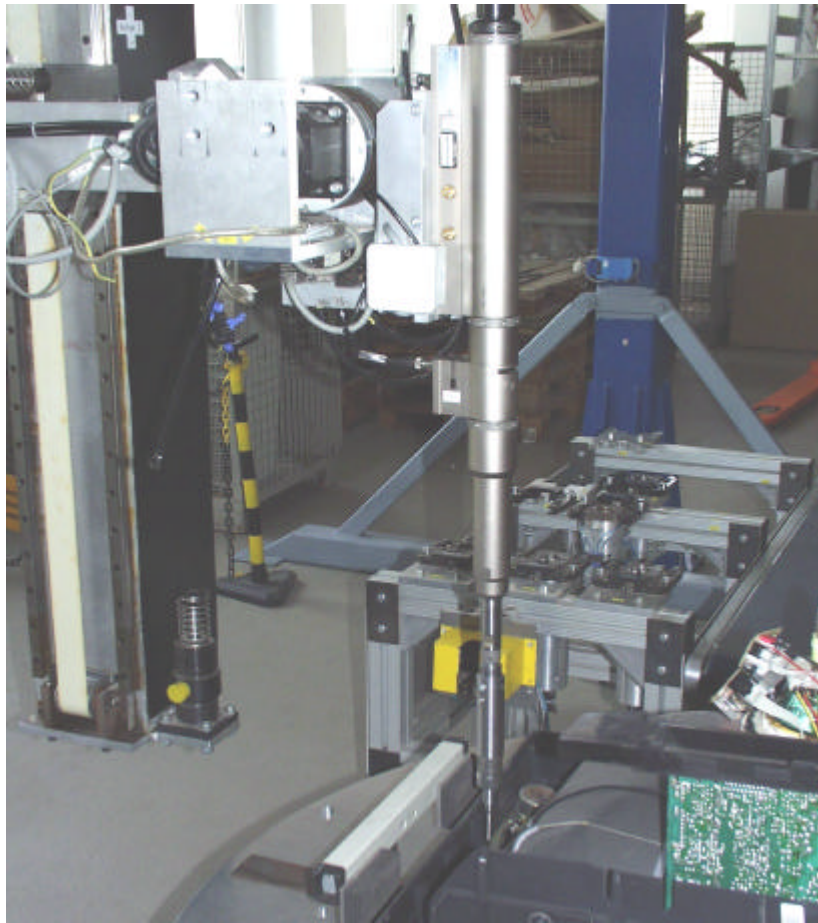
Integration des Schraubwerkzeugs mit Ausgleichsmodul in die Demontagezelle
